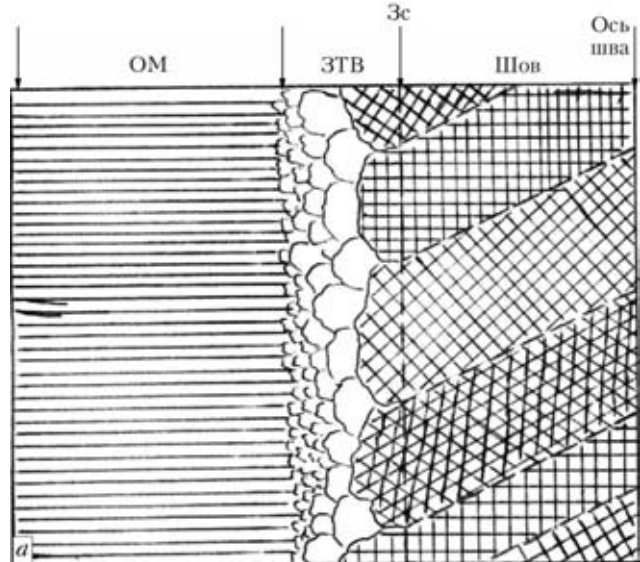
Макроструктура сварного соединения поликристаллического молибдена, выполненного дуговой сваркой
